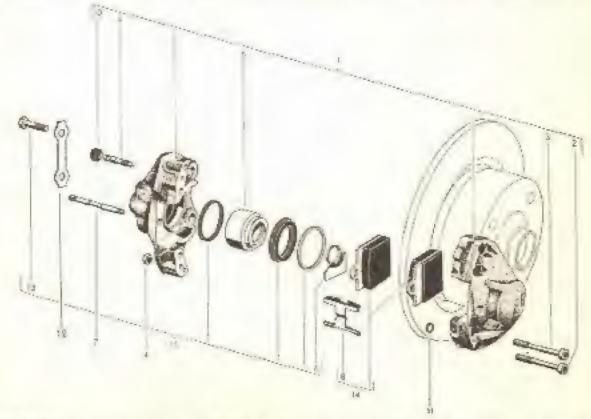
V — Componentes do freio a disco do sedan "1 600"; 1 — Cavalete fixo do freio a disco; 2, 3 — Parafusos cilindricos; 4 — Porca sextavada; 5 — Embolo de 40 mm; 6 — Chapa de retenção do êmbolo esquerdo; 7 — Pino de fixação das sapatas; 8 — Mola de retensão das sapatas; 9 — Parafuso de sangria; 10 — Coifa de proteção do parafuso de sangria; 11 — Junta; 12 — Chapa de segurança; 13 — Parafuso sextavado; 14 — Jôgo de sapatas ("pastithas") do freio a disco; 15 — Jōgo de vedação do freio a disco.
